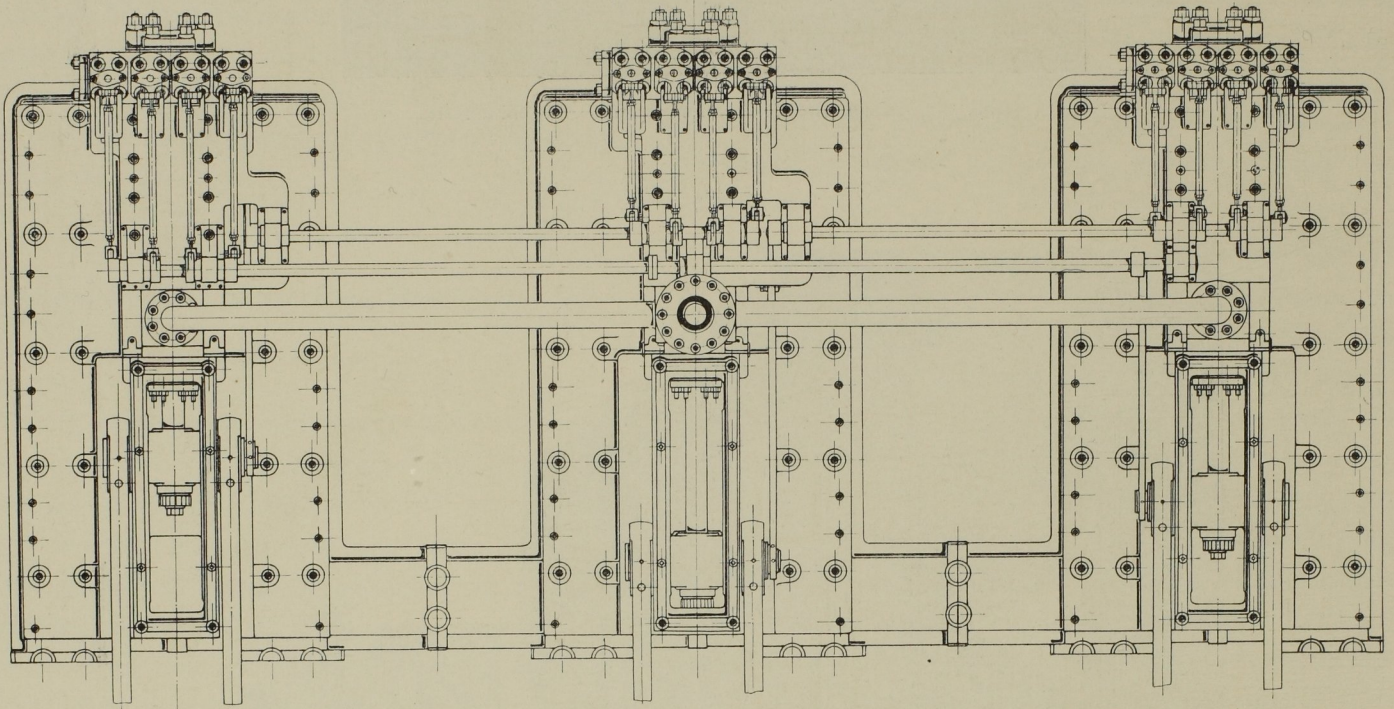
Grundriss der Presspumpen. Massst. 1:64.
